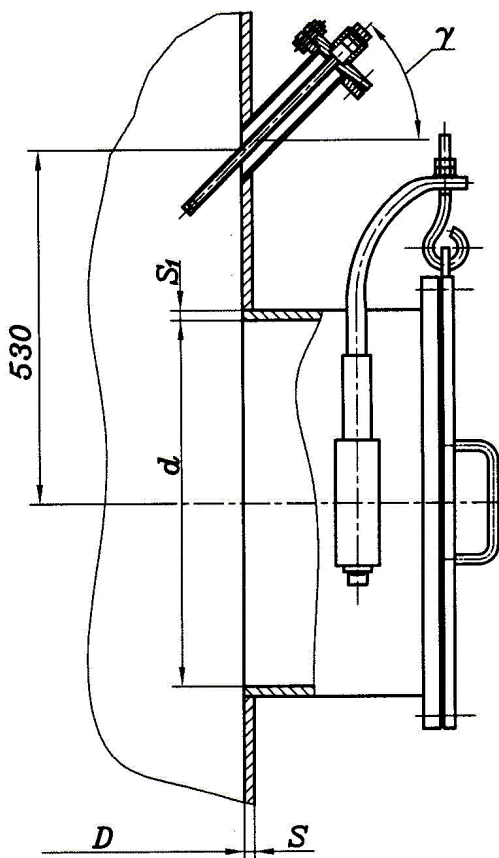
Розташування люка на циліндричній обичайці вертикального апарата
